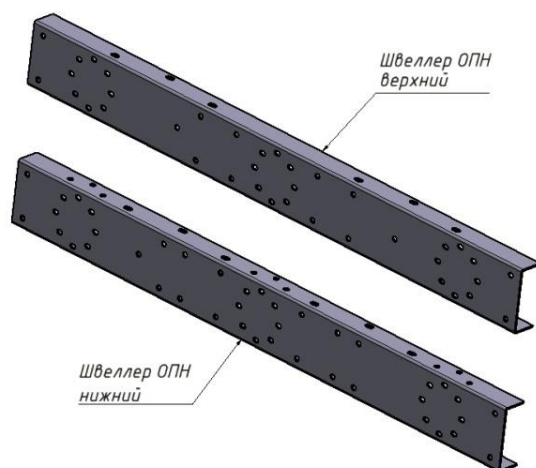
Различия верхнего и нижнего швеллера для установки ОПН
